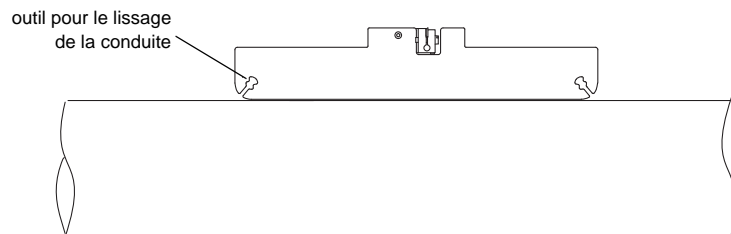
Contrôle de la planéité du point de mesure sur la conduite
